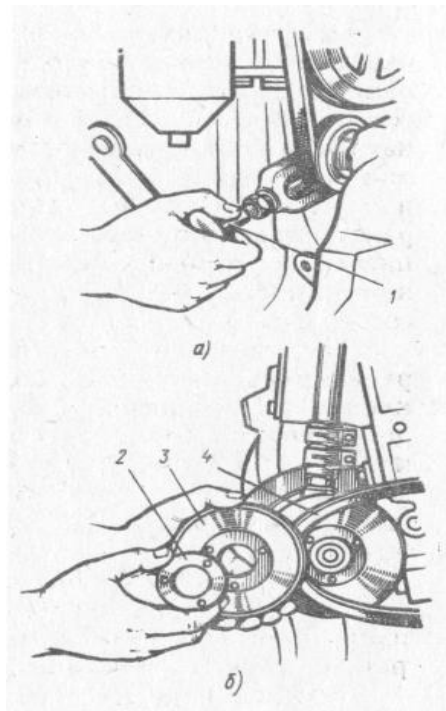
Регулировка натяжения ремней двигателя ЯМЗ-236:
